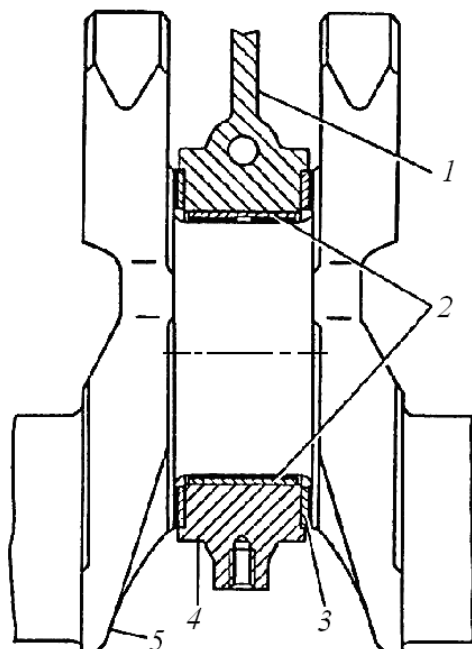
Средний (упорный) подшипник коленчатого вала: 1 – блок цилиндров; 2 – вкладыши подшипника; 3 – упорные полу-шайбы; 4 – крышка подшипника; 5 – коленчатый вал
